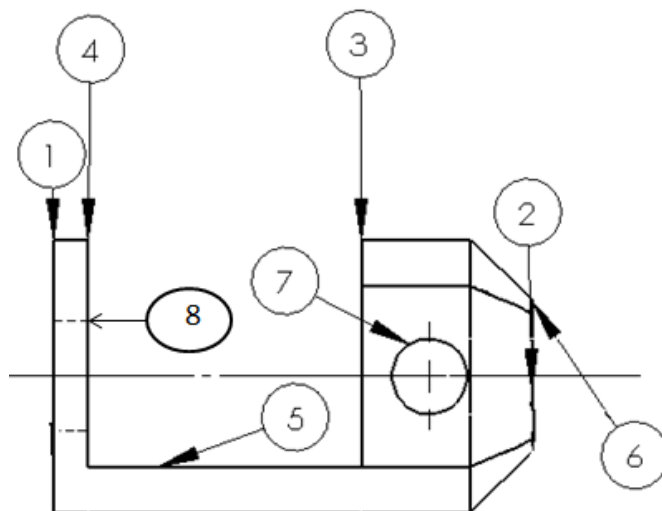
Numérotation des surfaces usinées de la pièce porte tige filetée
